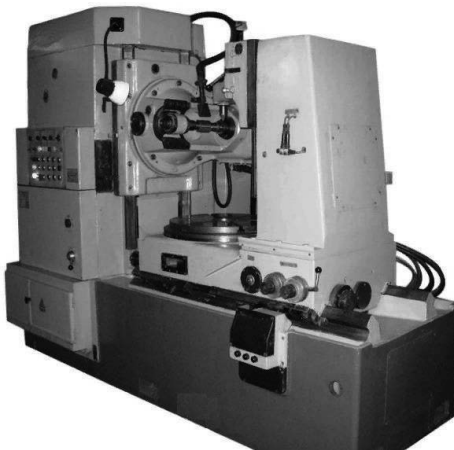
Зубофрезерний верстат і зона обробки зубчастого колеса
